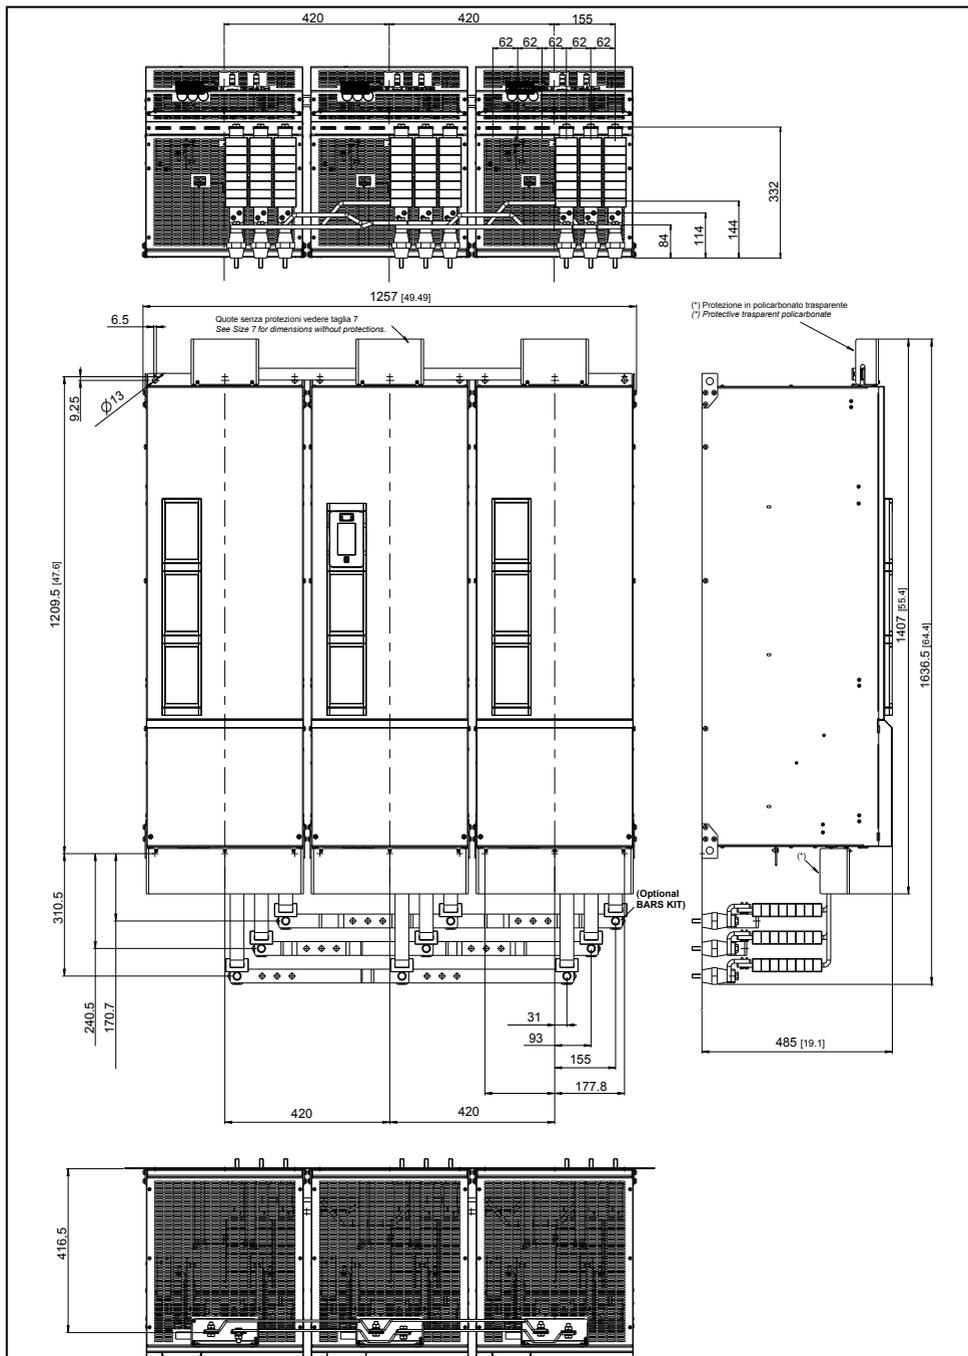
Dimensioni taglie 900 kW - 1 MW
